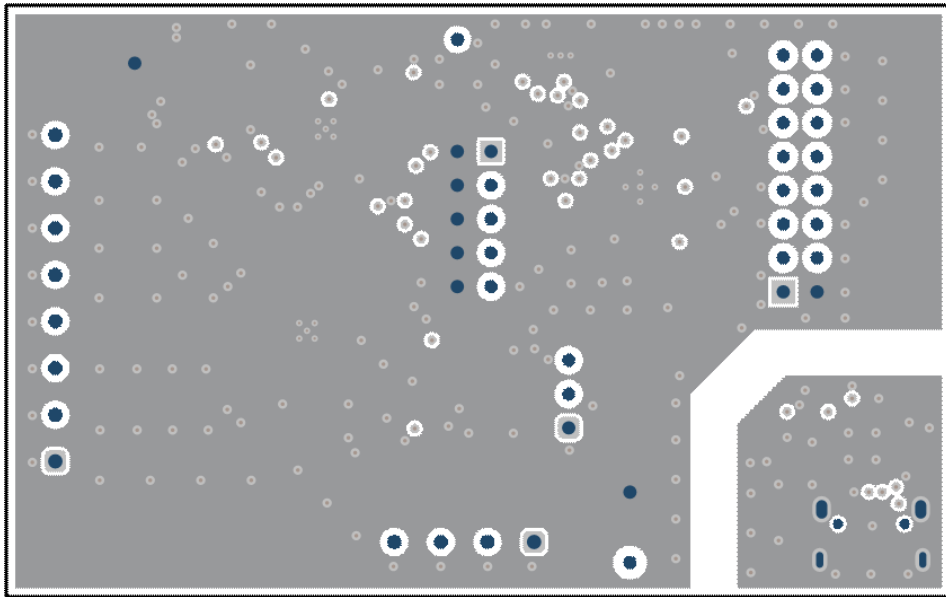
SNSR-DUAL-ADC-EVM PCB 布局 - 接地层 (第 1 层)
